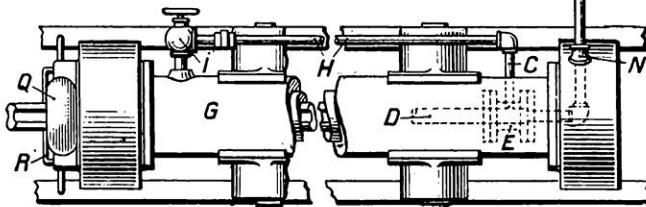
PLAN DE LA MACHINE POUR COULÉE ROTATIVE
